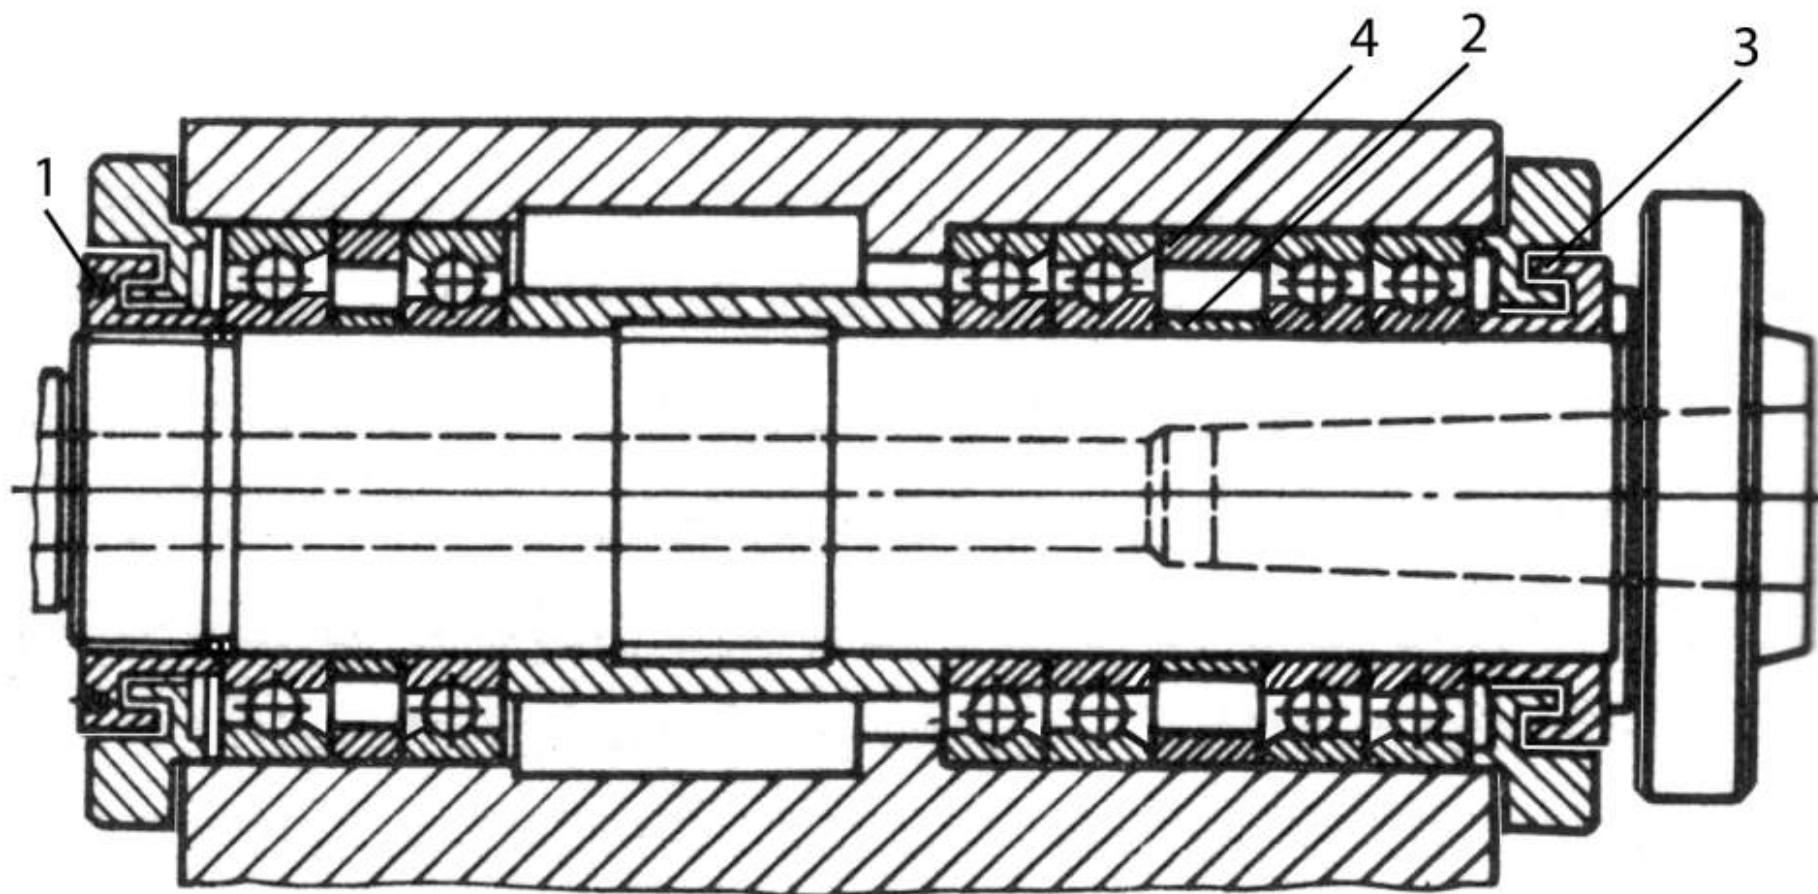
Шпиндельные узлы с радиально-упорными шарикоподшипниками типов 46000K×2 или 36000K×2 и 36000K):
